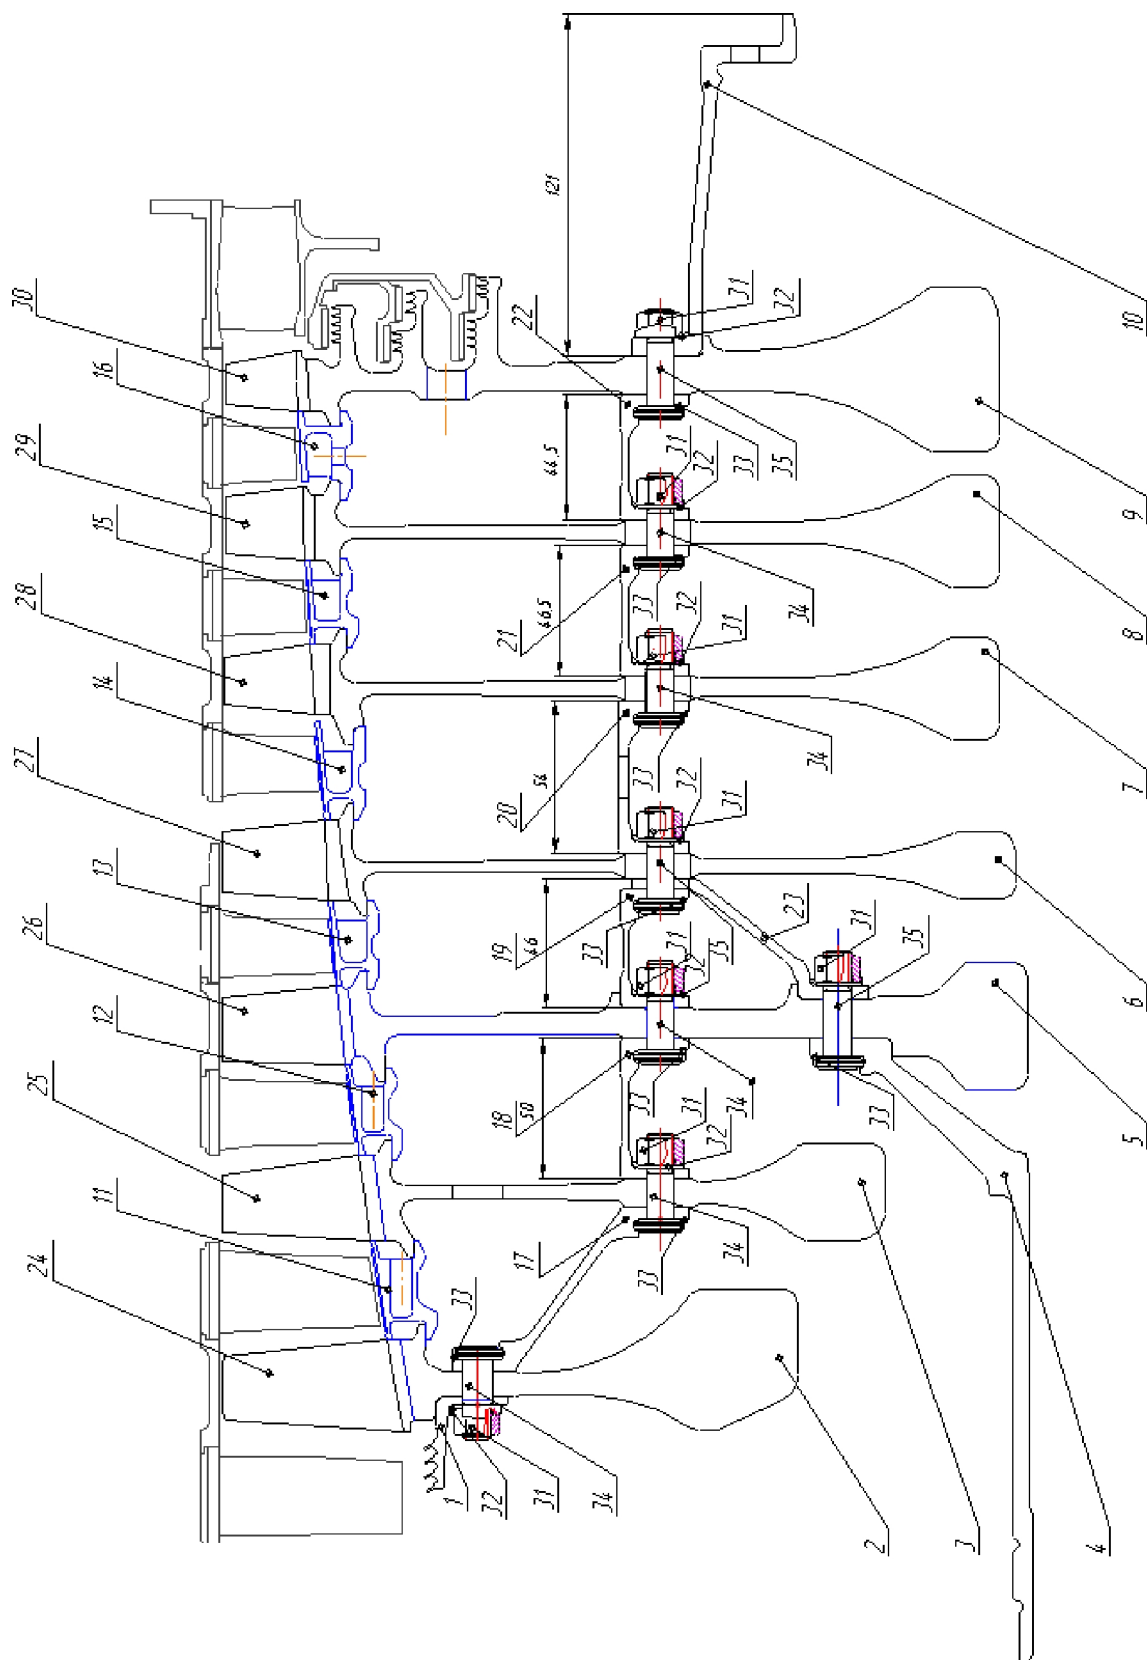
Продольный разрез компрессора высокого давления. двигателя НК-56
